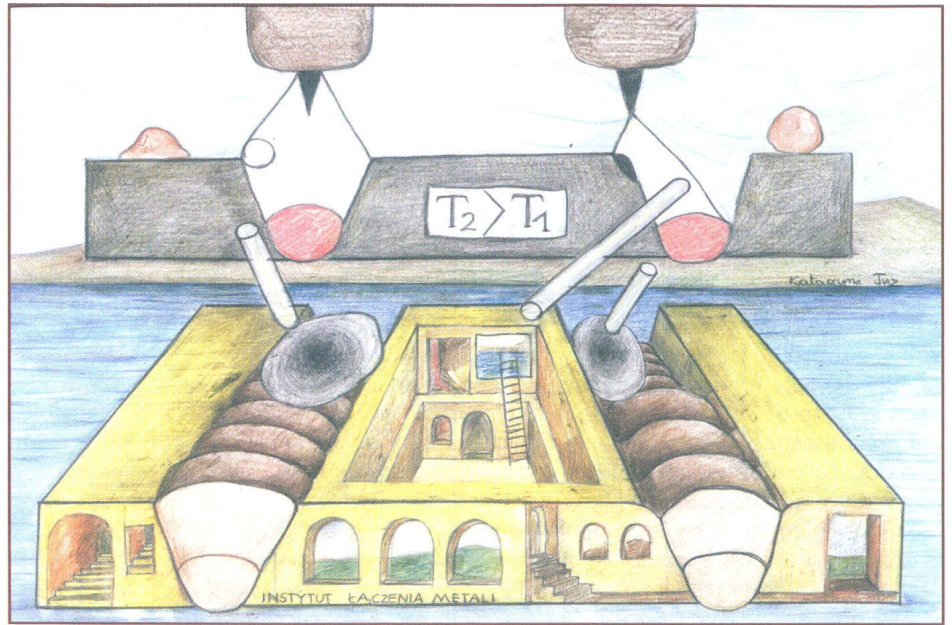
La diferencia entre la técnica de soldar materiales de poca y mucha conductividad térmica en la soldadura TIG
